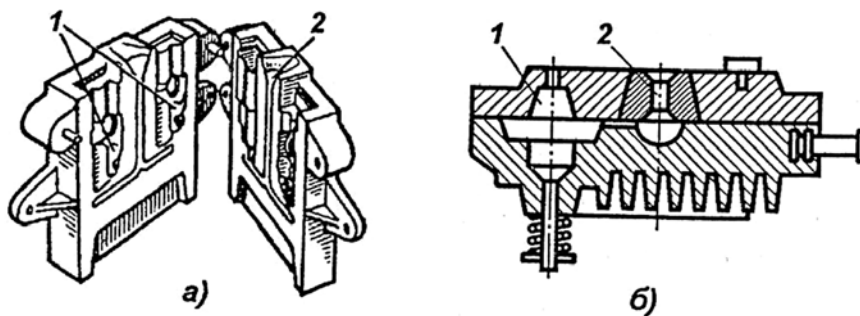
Конструктивные формы кокилей: а – с вертикальным разъемом; б – с горизонтальным разъемом; 1 – форма гнезда для отливки детали; 2 – литниковая система
